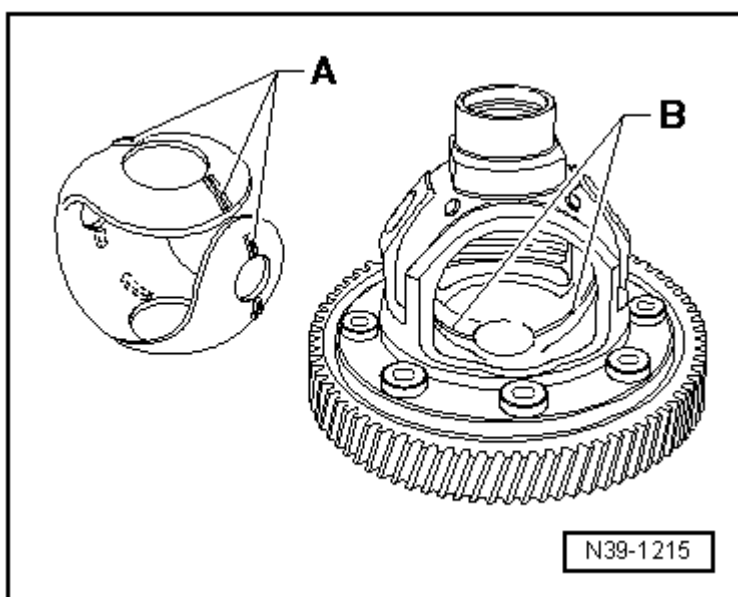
安装差速器锥形行星齿轮和差速器锥齿轮轴
